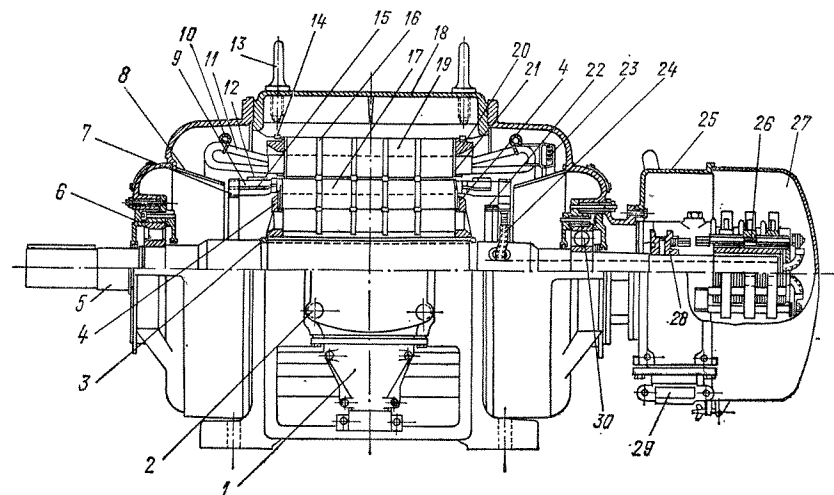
Трехфазный асинхронный двигатель с фазным ротором 180 кВт, 975 об/мин
